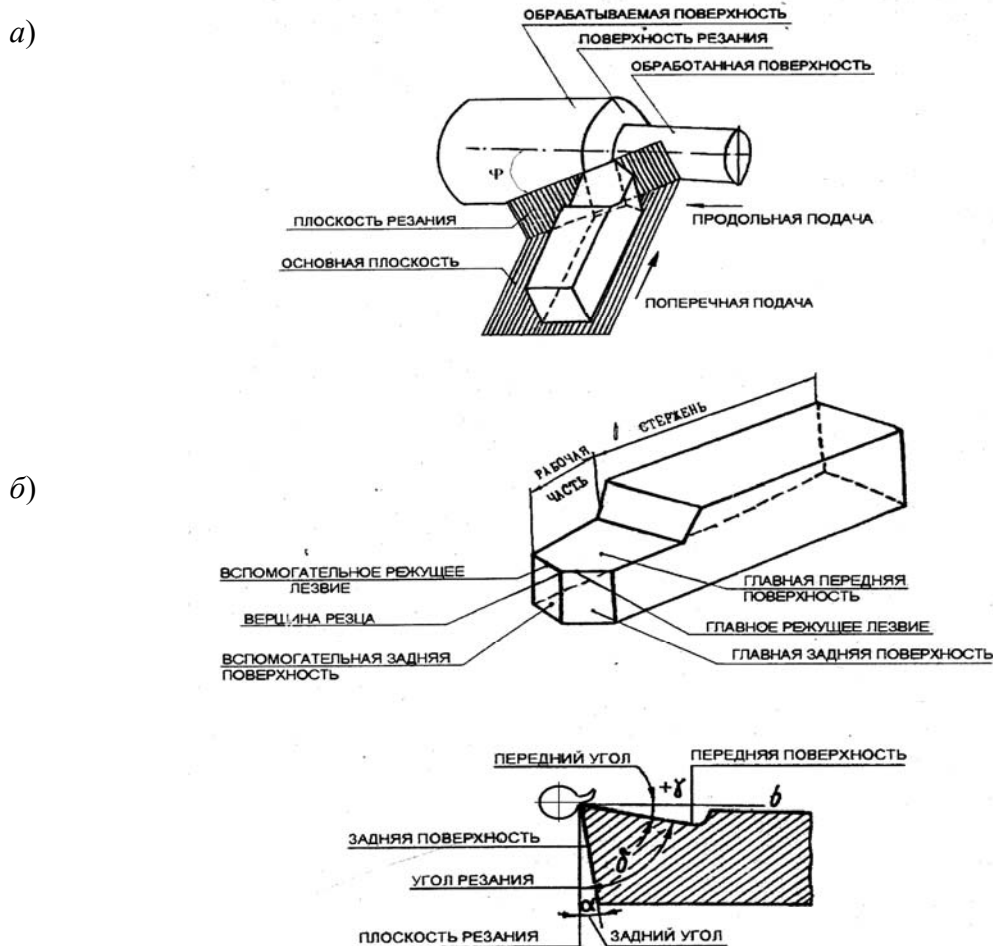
Поверхности на обрабатываемой заготовке, координатные плоскости, геометрические параметры реза
